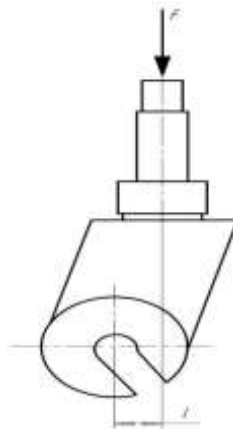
Розрахункова схема вилки поворотного колеса
